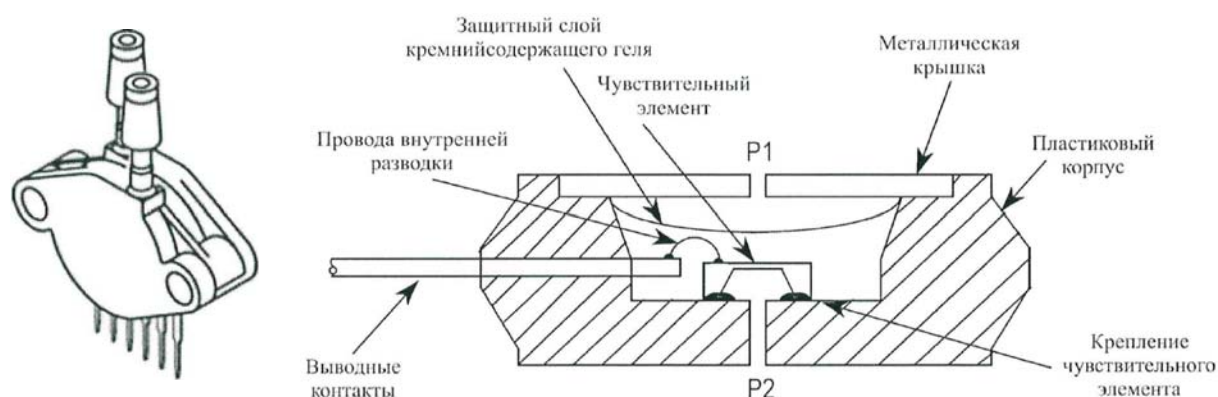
Преобразователь давления с выходными портами: а – внешний вид; б – внутренне устройство
